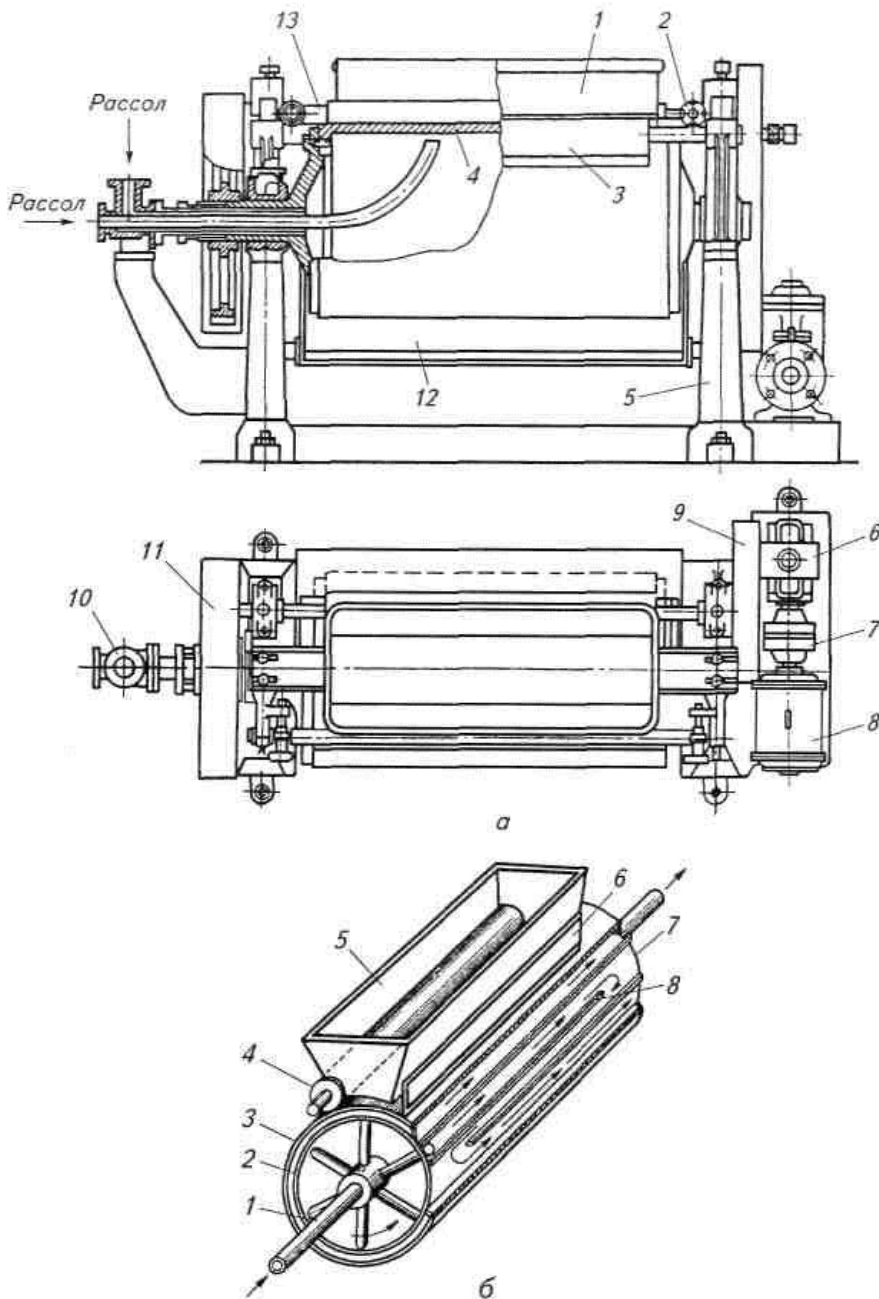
Барабанный охладитель открытого типа: а — общий вид: 1 — бункер; 2 — штурвал; 3 — нож для съема творога; 4 — барабан; 5 — опоры; 6 — редуктор; 7 — муфта; 8 — электродвигатель; 9, 11 — кожухи; 10 — патрубок для входа рассола; 12 — приемная ванна; 13 — распределительный валик; б — барабан: 1 — цапфы; 2 — вытеснитель; 3 — барабан; 4 — распределительный валик; 5 — бункер; 6 — нож; 7 — перегородка; 8 — ребра
